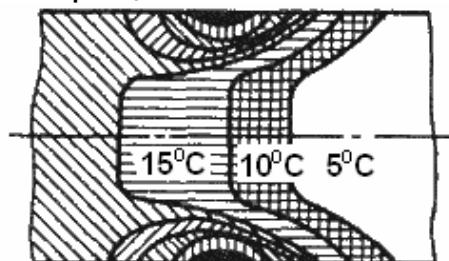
Теплове поле, що рухається перед джерелом теплоти в поверхневих шарах заготовки
